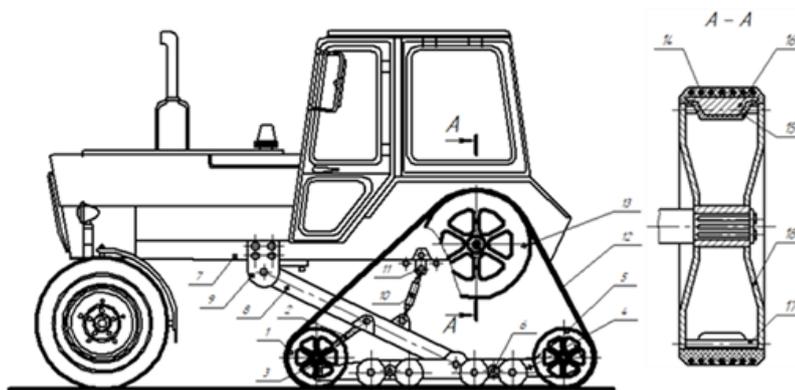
Полугусеничный движитель с резиноармированными гусеницами
